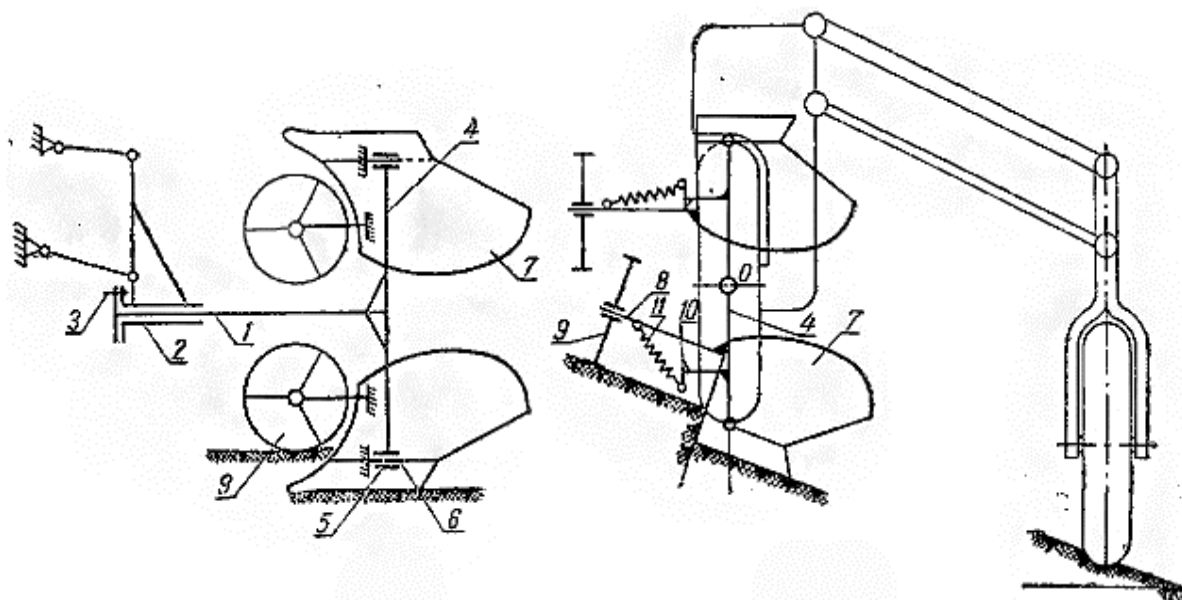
Плуг гірський обертовий, одноборозний, навісний [56]
